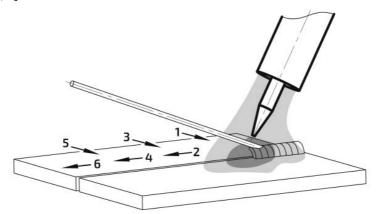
Пример манипуляции присадочной проволокой при TIG сварке.
